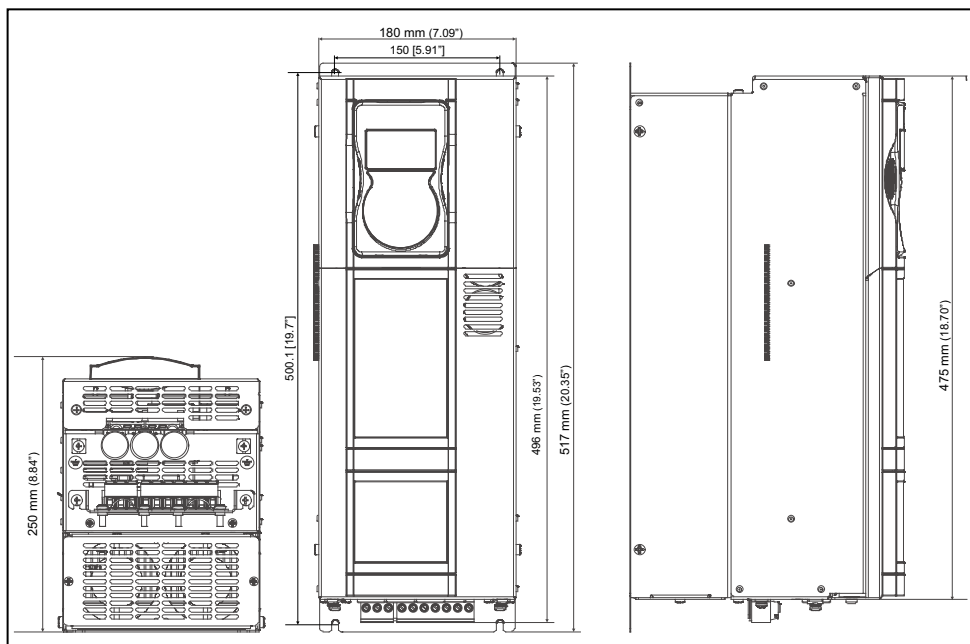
Размеры для типоразмера 3 (ADV200-...-4-DC)
